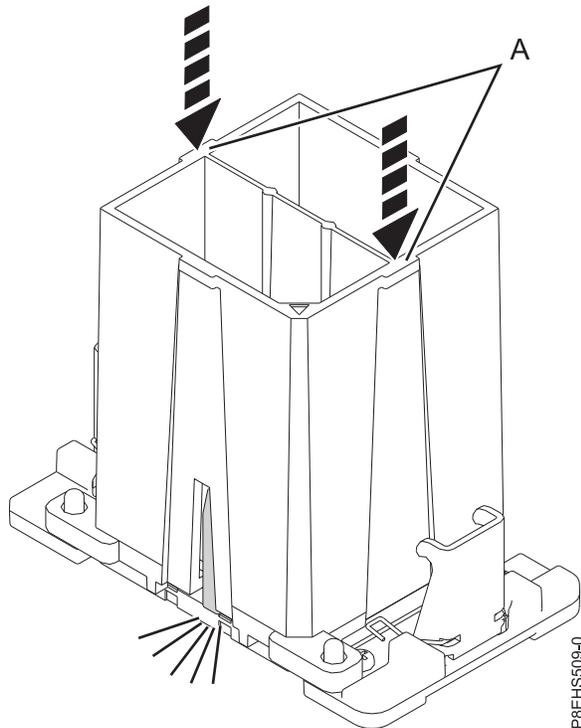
Systemprozessormodul im Werkzeug einrasten lassen
